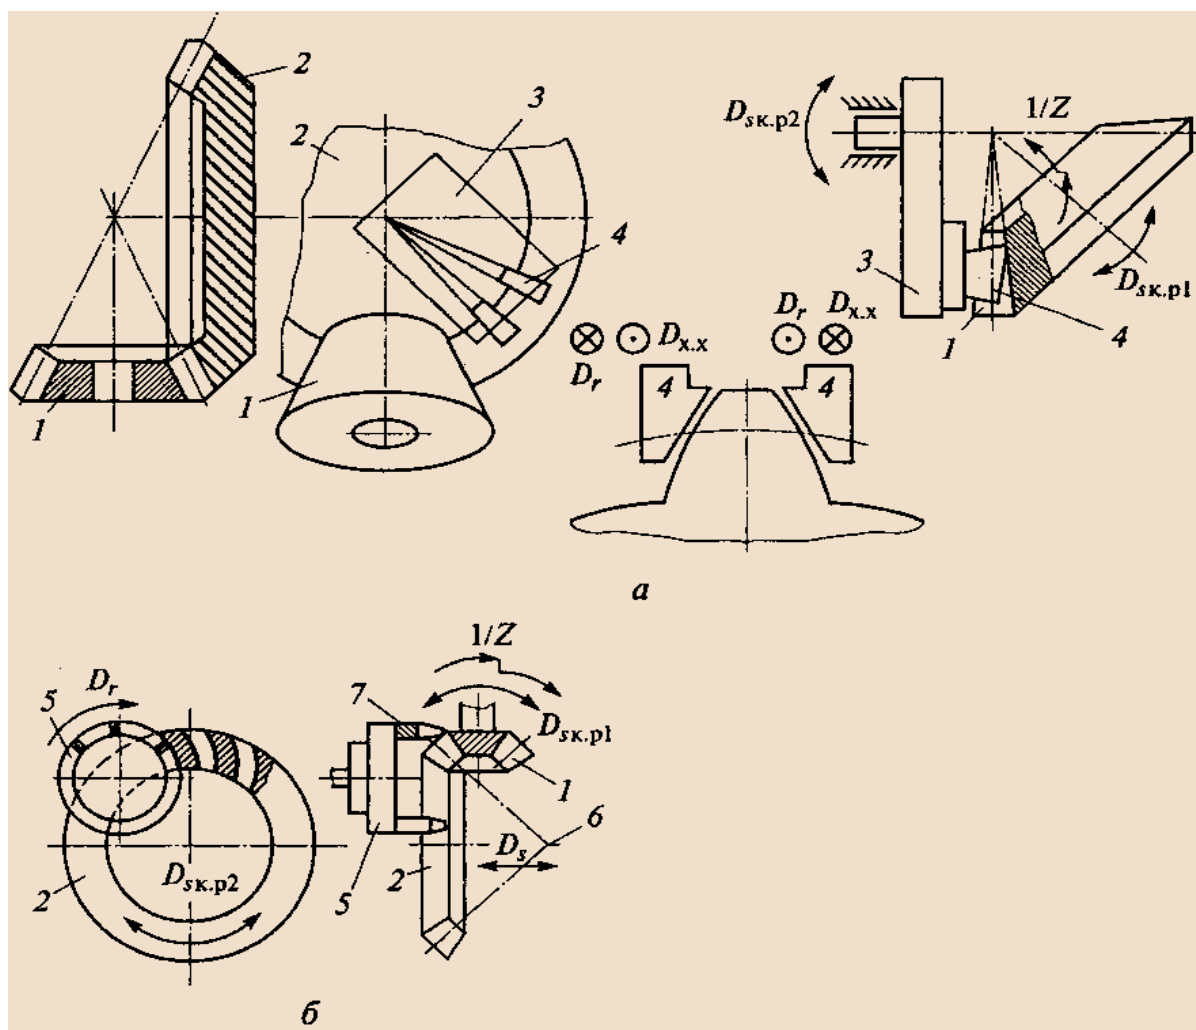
Обработка конических зубчатых колёс зубостроганием (а) и круговой резцовый головкой (б):
